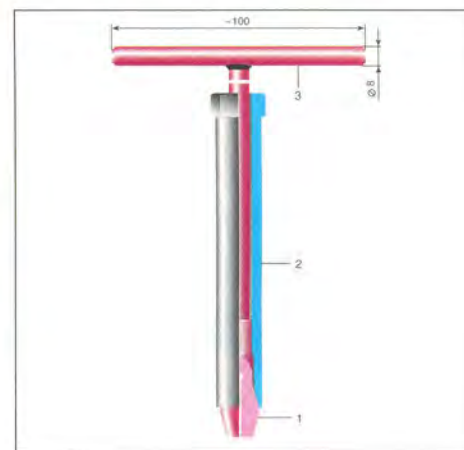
Приспособление с цанговым зажимом стержня: 1 – цанга; 2 – втулка с гайкой; 3 – рукоятка.
